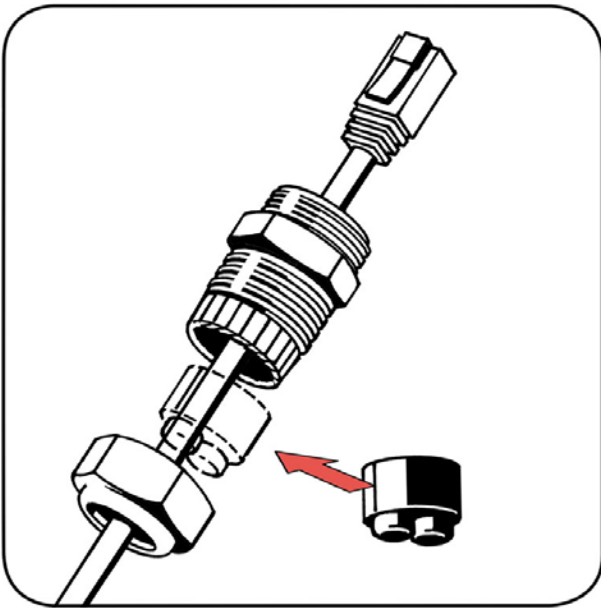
Kabelführung durch Kabelverschraubungen
